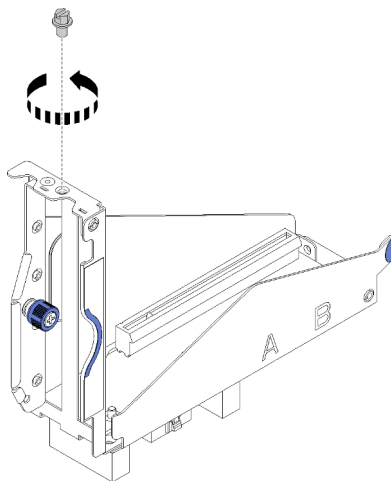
Entfernen der Schraube vom Adapterrahmen
